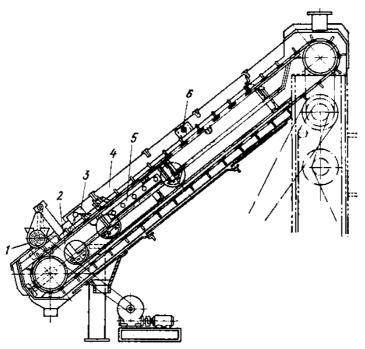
Стрічковий розварювач: 1 – шнек; 2 – стрічка; 3, 6 – душові пристрої; 4 – корпус; 5 – труби
